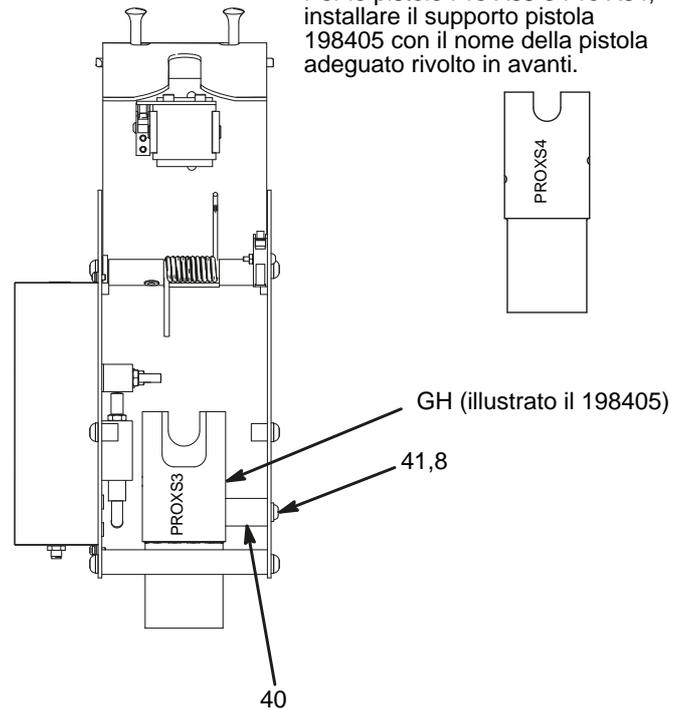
Installazione del supporto pistola (pistole Pro Xs3 e Xs4)
